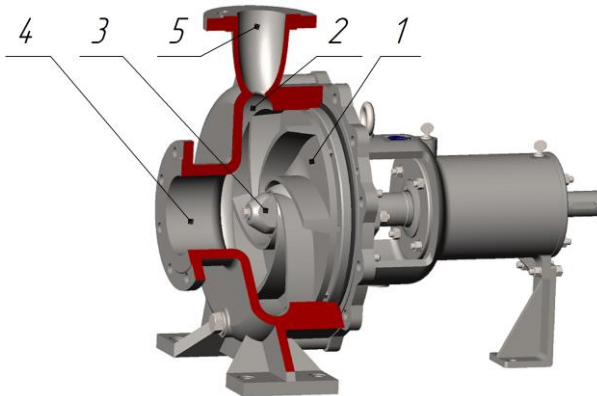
Конструкція вільновихрового насоса: 1 – робоче колесо; 2 – вільна камера (ВК); гайка-обтікач; 4 – всмоктувальний патрубков; 5 – напірний патрубков.
